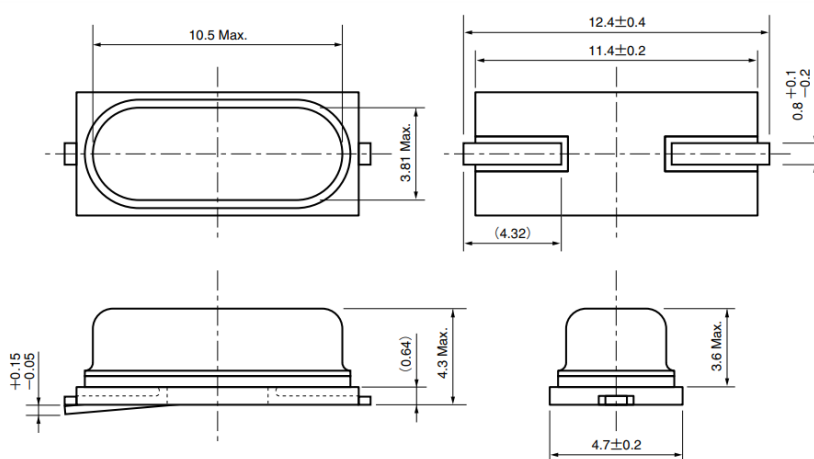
Зовнішній вигляд та габаритні розміри кварцевого резонатора КХ-К в корпусі HC-49/S-SMD
